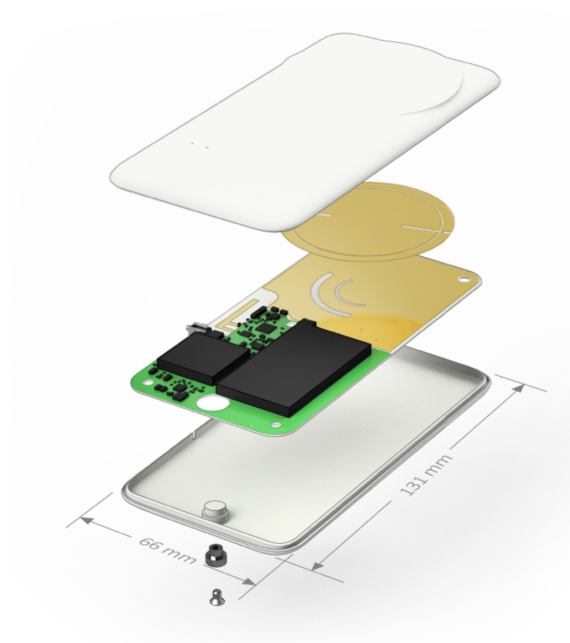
Explosivo con dimensiones de los Airtags de CleanSpace [20]
